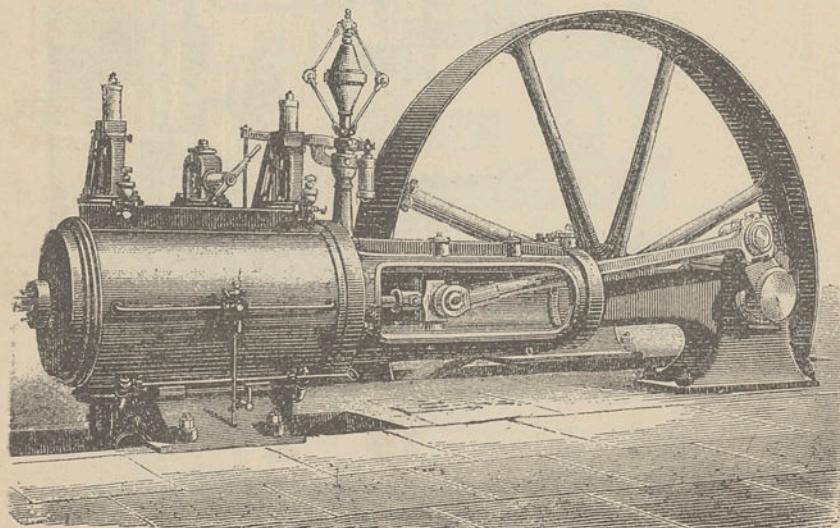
MACHINA HORIZONTAL COM DISTRIBUIÇÃO SULZER
